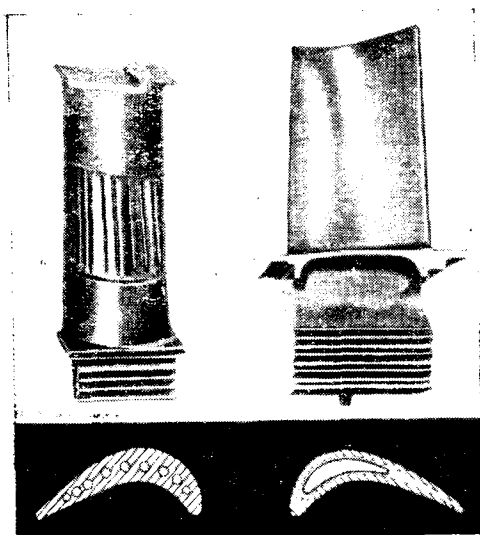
Рабочая лопатка турбины высокого давления двигателя Р-100 старой (слева) и новой конструкции
